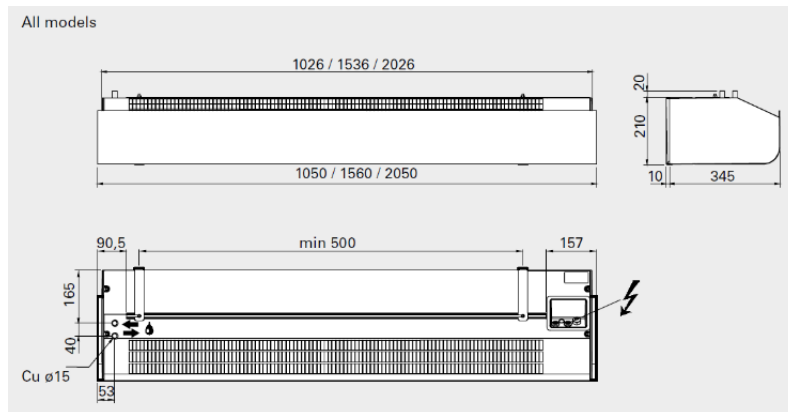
Desenho técnico da cortina de ar PA2515A da FRICO [58]
